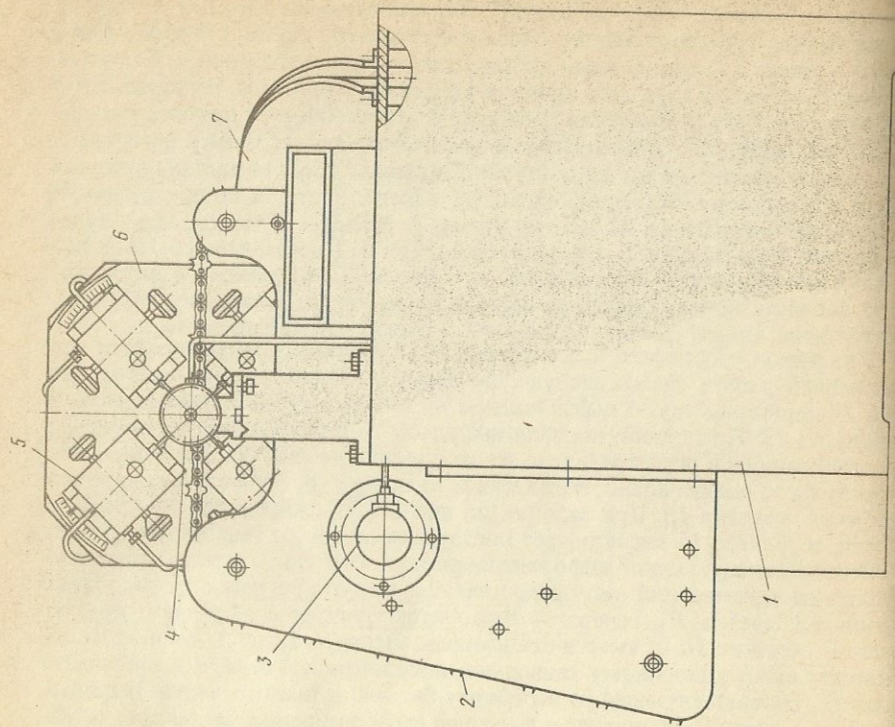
Автомат для сортировки зубчатых колес с числом зубьев $z > 50$
